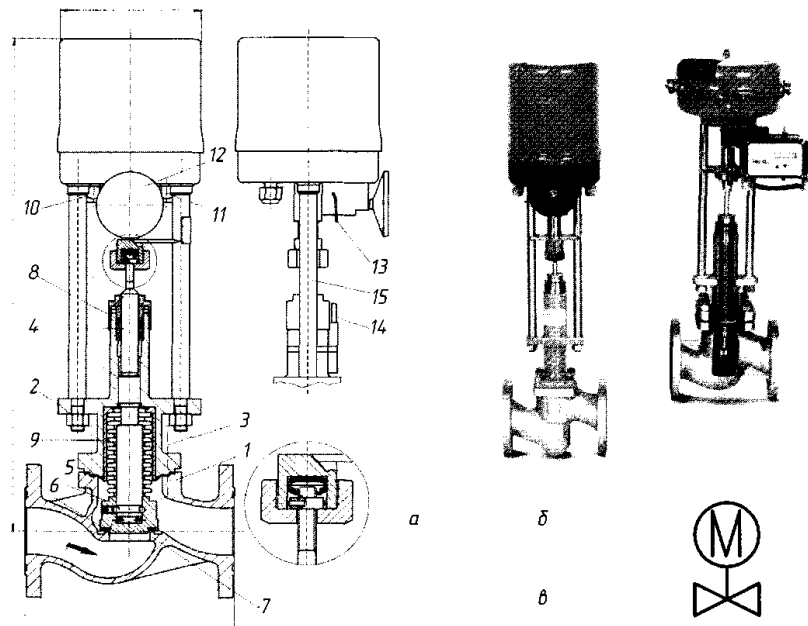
Моторные вентили: *a* — устройство: 1 — корпус, 2 — верхняя часть, 3 — болты, 4 — шпindel, 5 — клапан, 6 — уплотнение клапана, 7 — седло, 8 — уплотнение, 9 — сильфон, 10, 11 — сальники подключения кабеля, 12 — маховик, 13 — рычаг ручного управления, 14 — обогрев шпинделя, 15 — стойка; *b* — внешний вид моторных вентилях; *v* — условное обозначение
